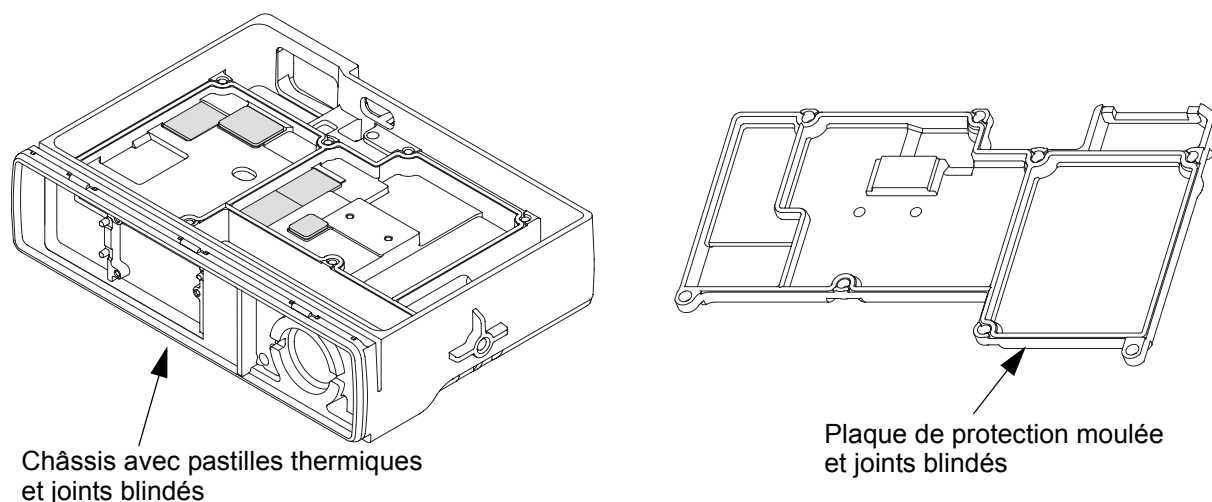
Pastilles thermiques et joints blindés sur le châssis et la plaque de protection moulée
